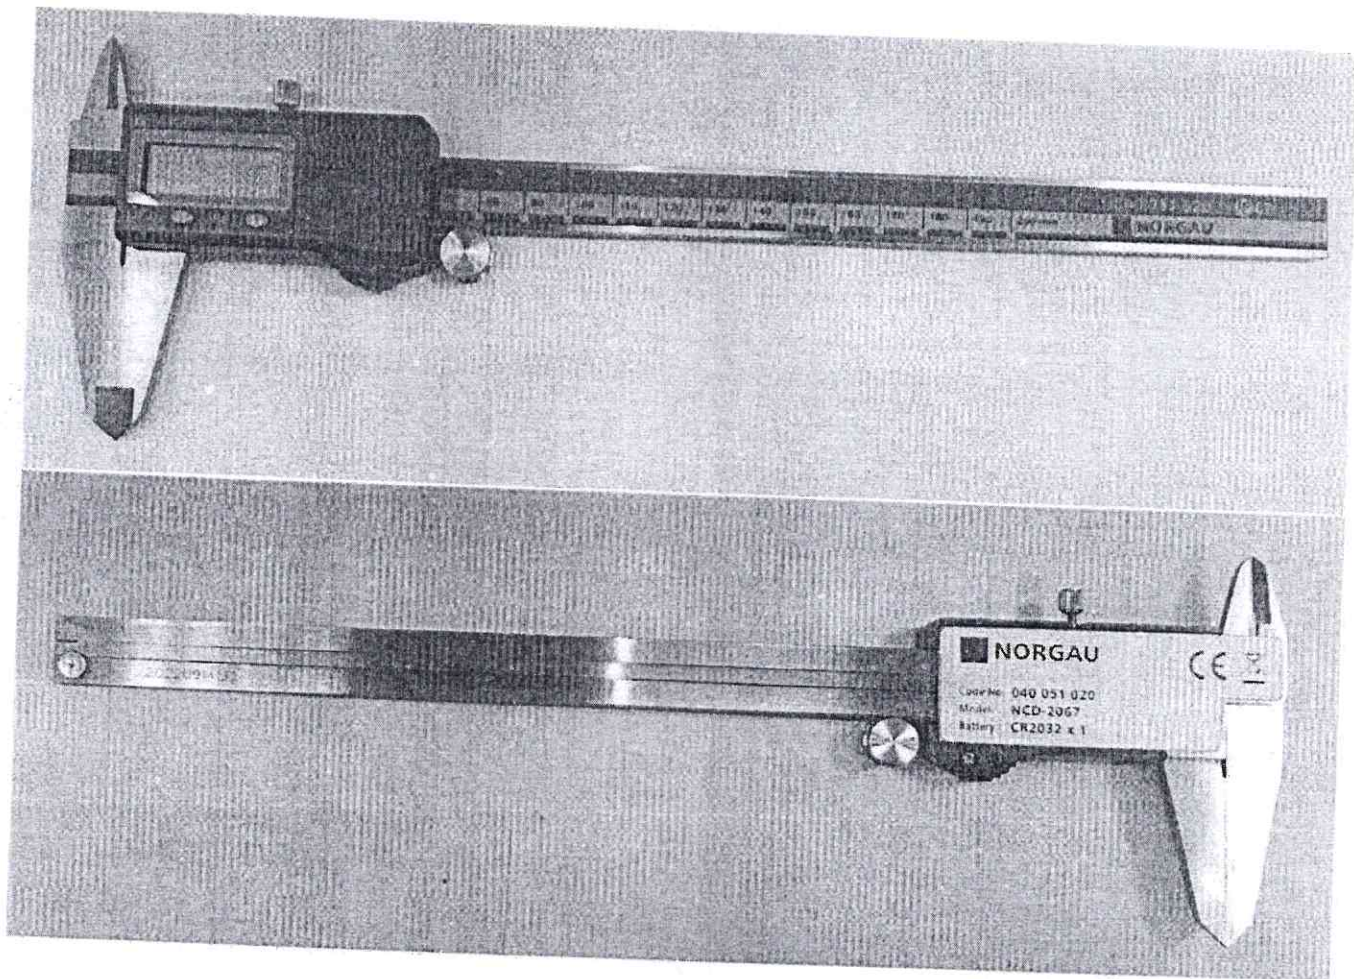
Общий вид штангенциркулей с цифровым отсчетным устройством во влаго- и пылезащитном исполнении двусторонние с глубиномером
